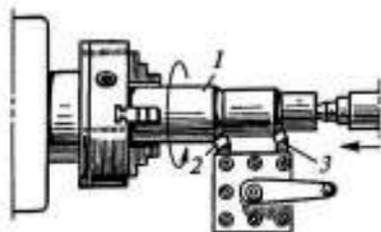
Установка заготовок в патроне с поджимом задним центром:
